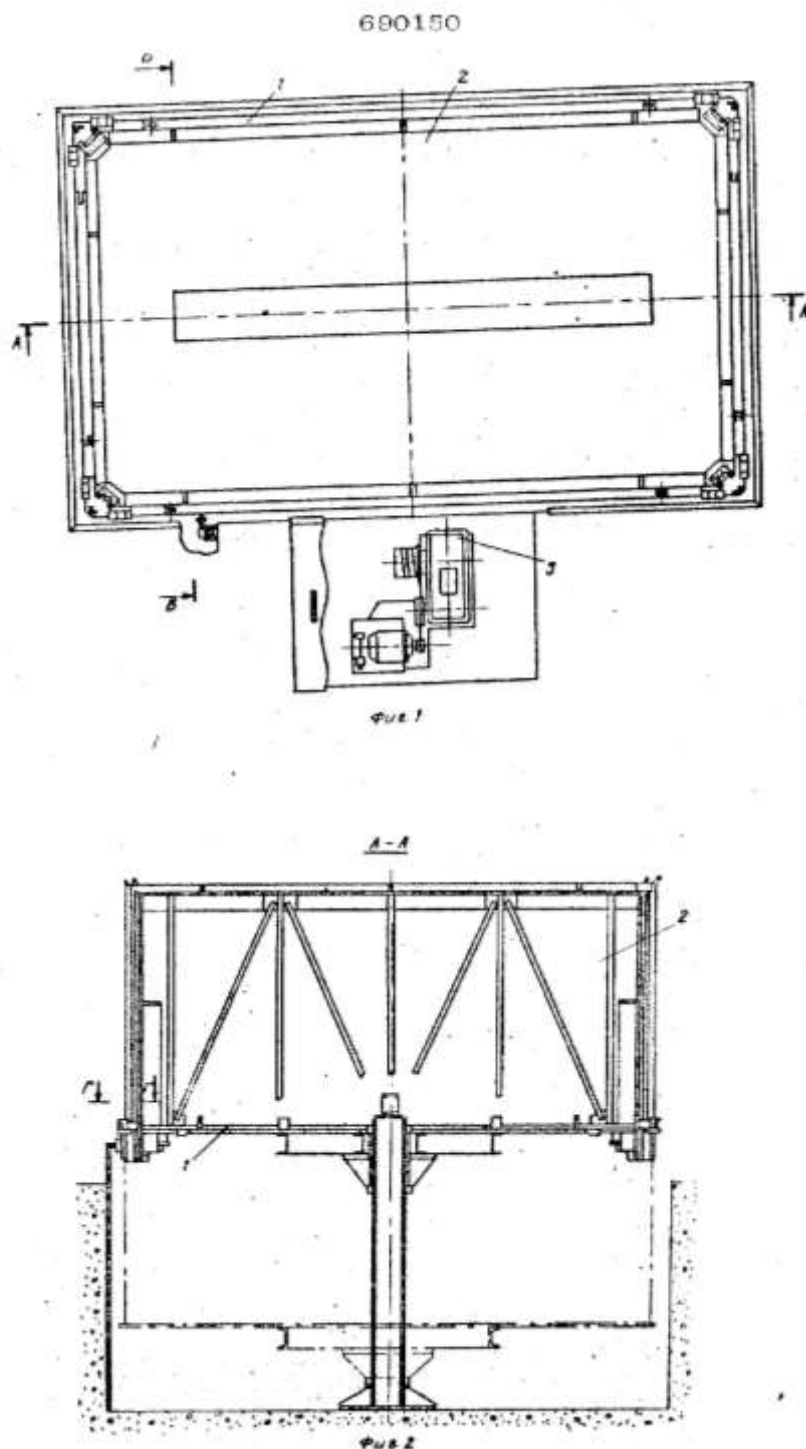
Кондуктор с условно-прозрачными стенками корпуса вид сверху и разрез.
